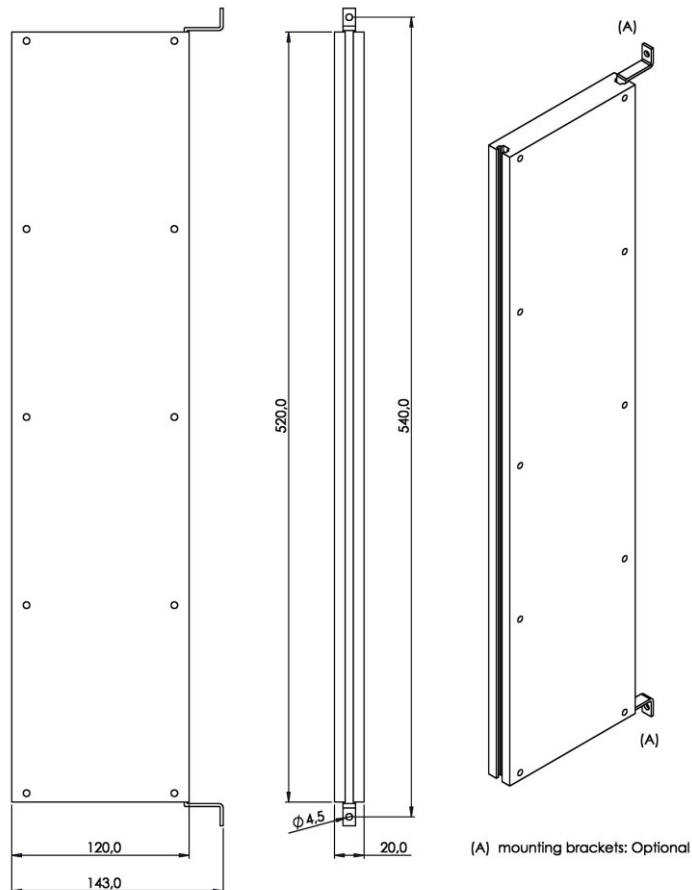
Dimensioni resistenza di frenatura UL / UL braking resistor dimensions
